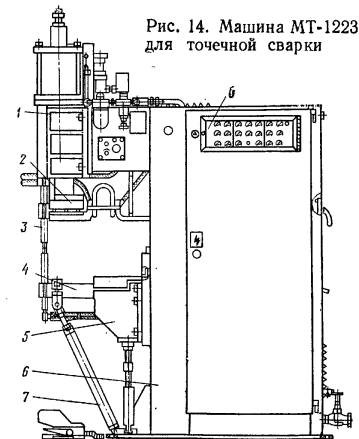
Машина МТ-1223 для точечной сварки
